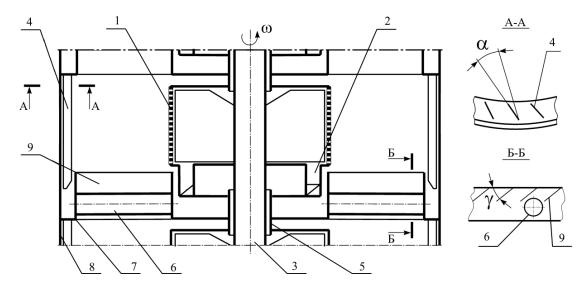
Схема контактного элемента роторного распылительного аппарата: 1 – диспергирующее устройство; 2 – заборное устройство; 3 – вал; 4 – пристенный калеотбойник; 5 – переливная труба; 6 – переточная труба; 7 – тарелка; 8 – корпус; 9 – направляющие лопатки
